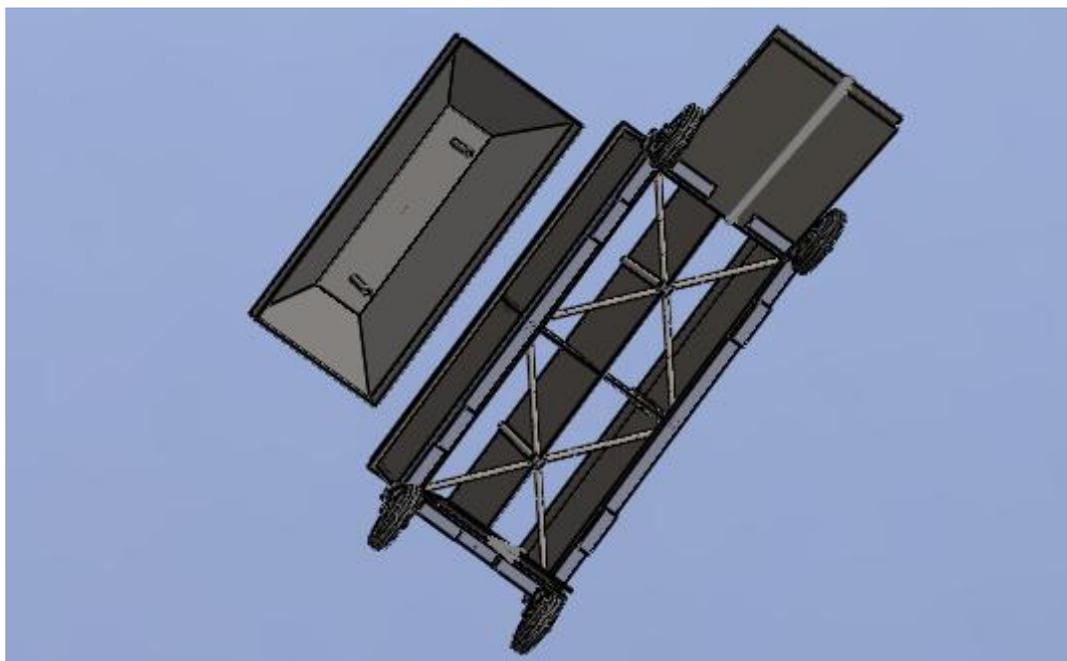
Esboço da caixa de extinção a seco, vista do fundo, com a tampa.
